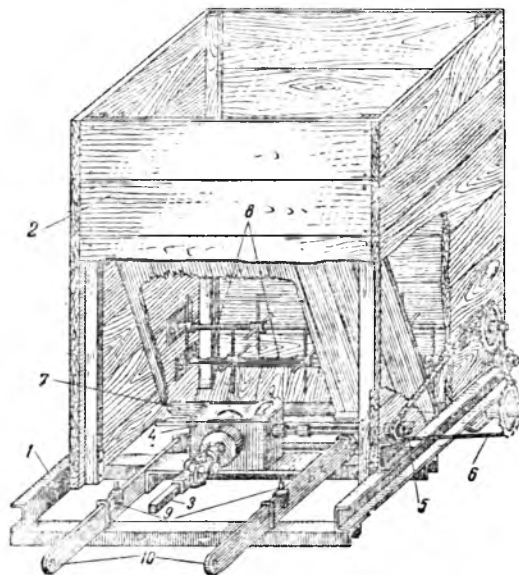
Детали мульчирователя: 1 — рама; 2 — бункер; 3 — шарнирная передача от вала отбора мощности трактора; 4 — передаточная коробка; 5 — вал передаточной коробки с ведущей звездочкой; 6 — цепь; 7 — выбрасывающий (высевающий) аппарат; 8 — ворошилка; 9 — тяги к рычагам гидроподъемника; 10 — отверстия для крепления к трактору.
